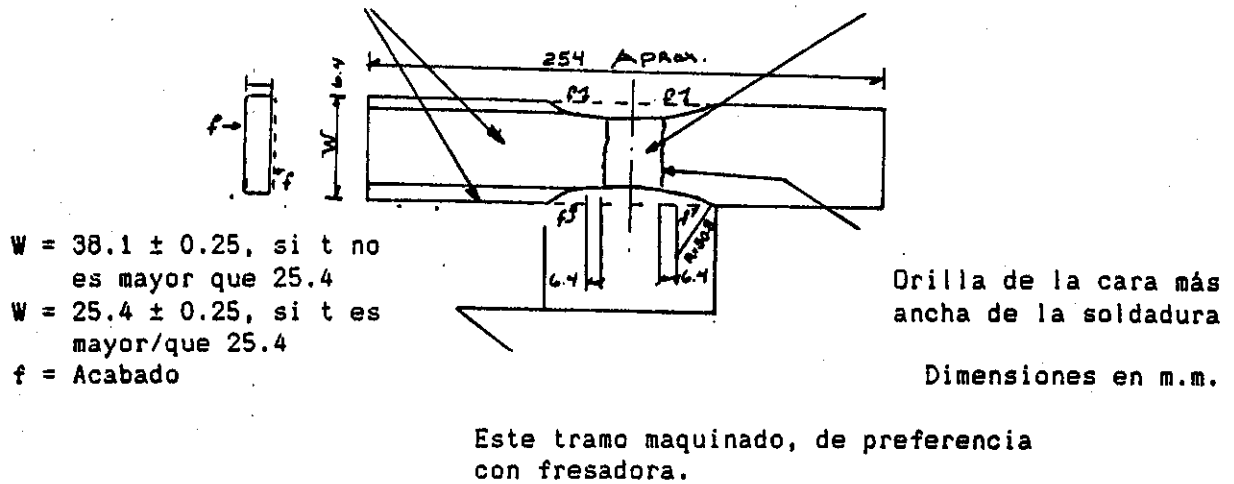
FIG. A- ESPECIMEN DE SECCION REDUCIDA PARA PRUEBA DE TENSION
